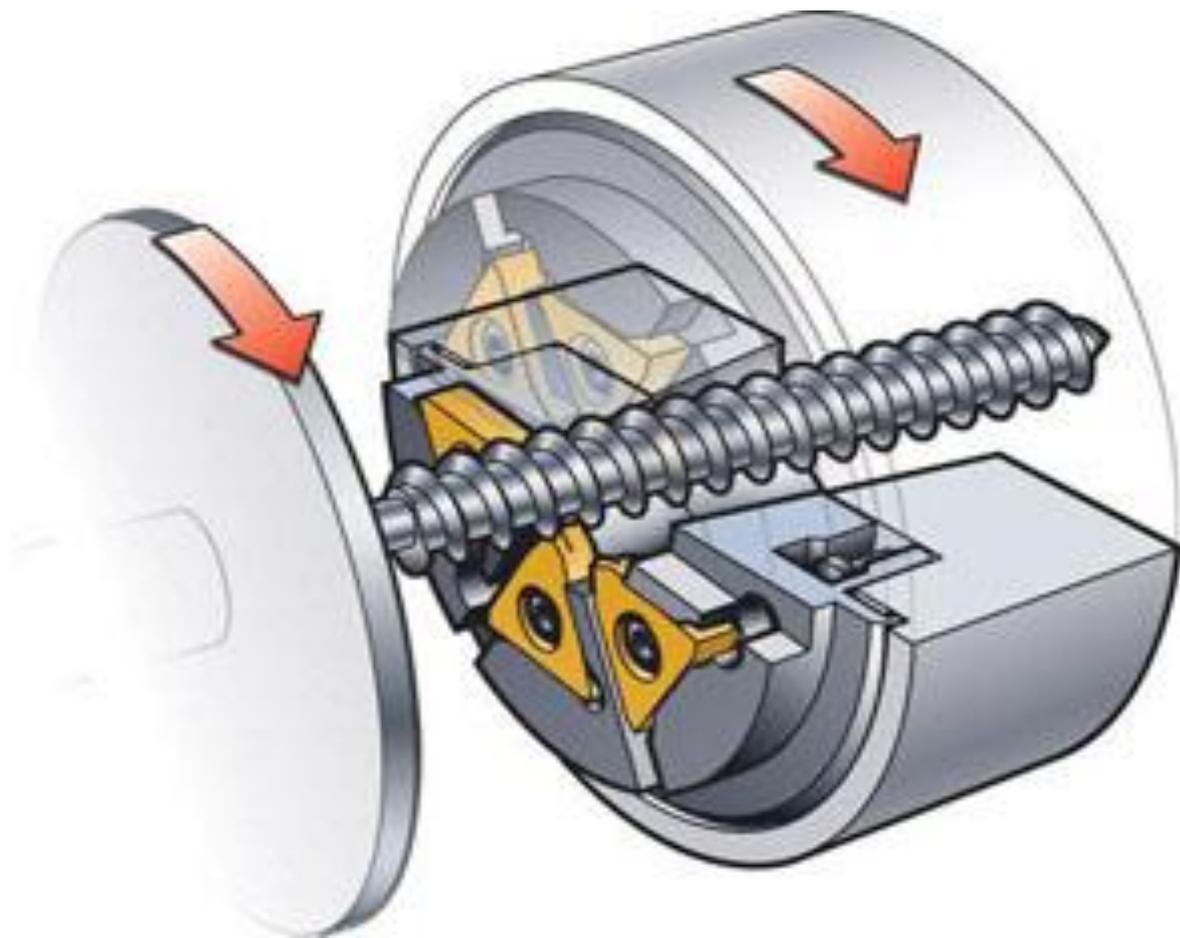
Схема нарезания наружной резьбы вращающейся резцовой головкой
